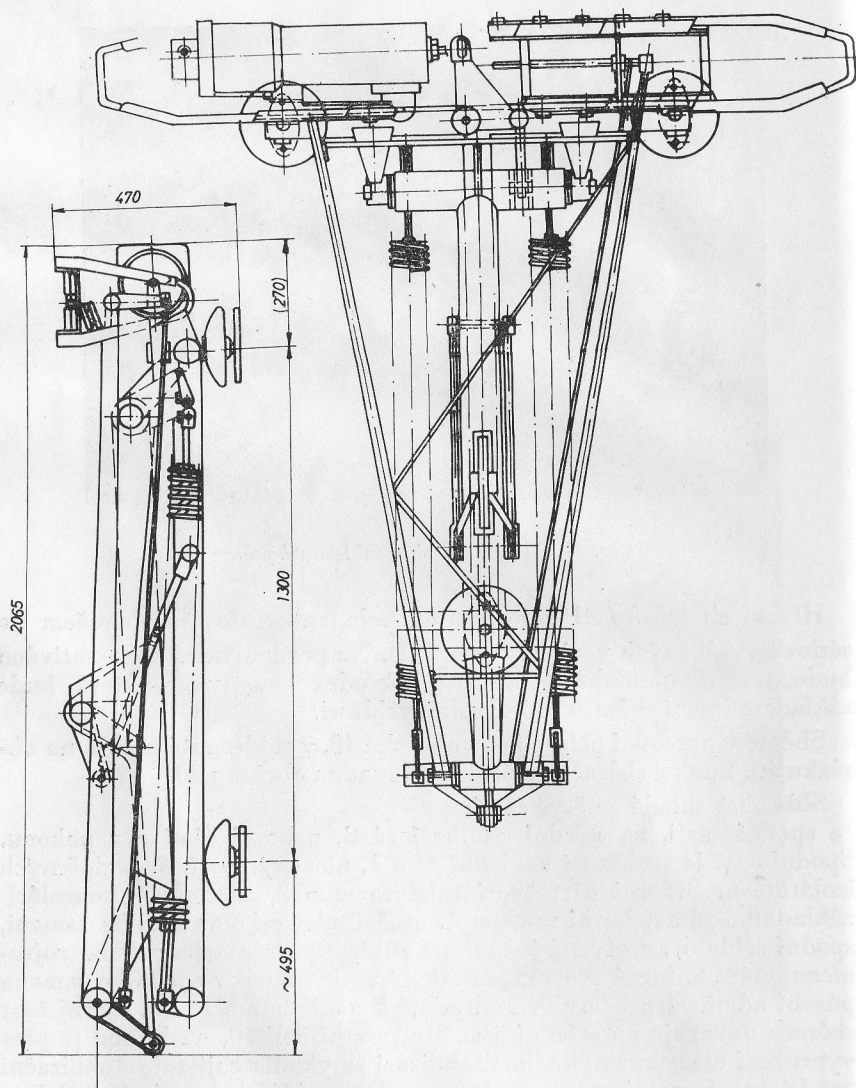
Hlavní sběrač v zaklesnuté poloze
